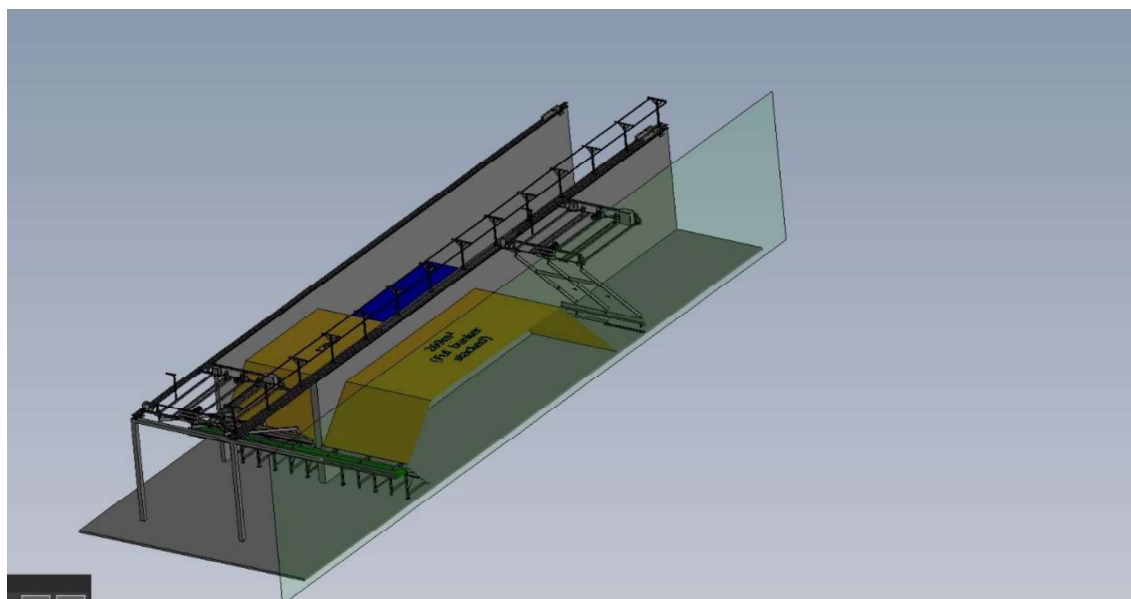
Silos de armazenamento de biomassa tipo TopLoader.
